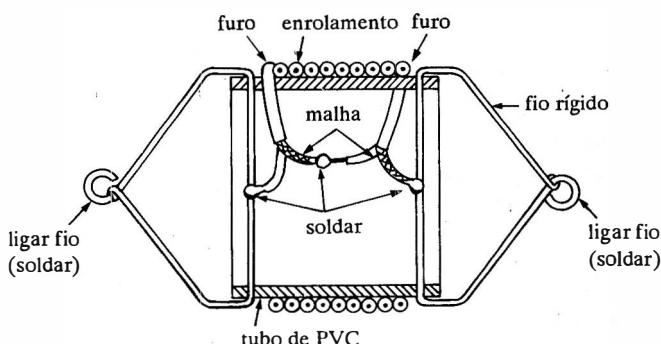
Arranjo físico da bobina de corte confeccionada de cabo coaxial.
